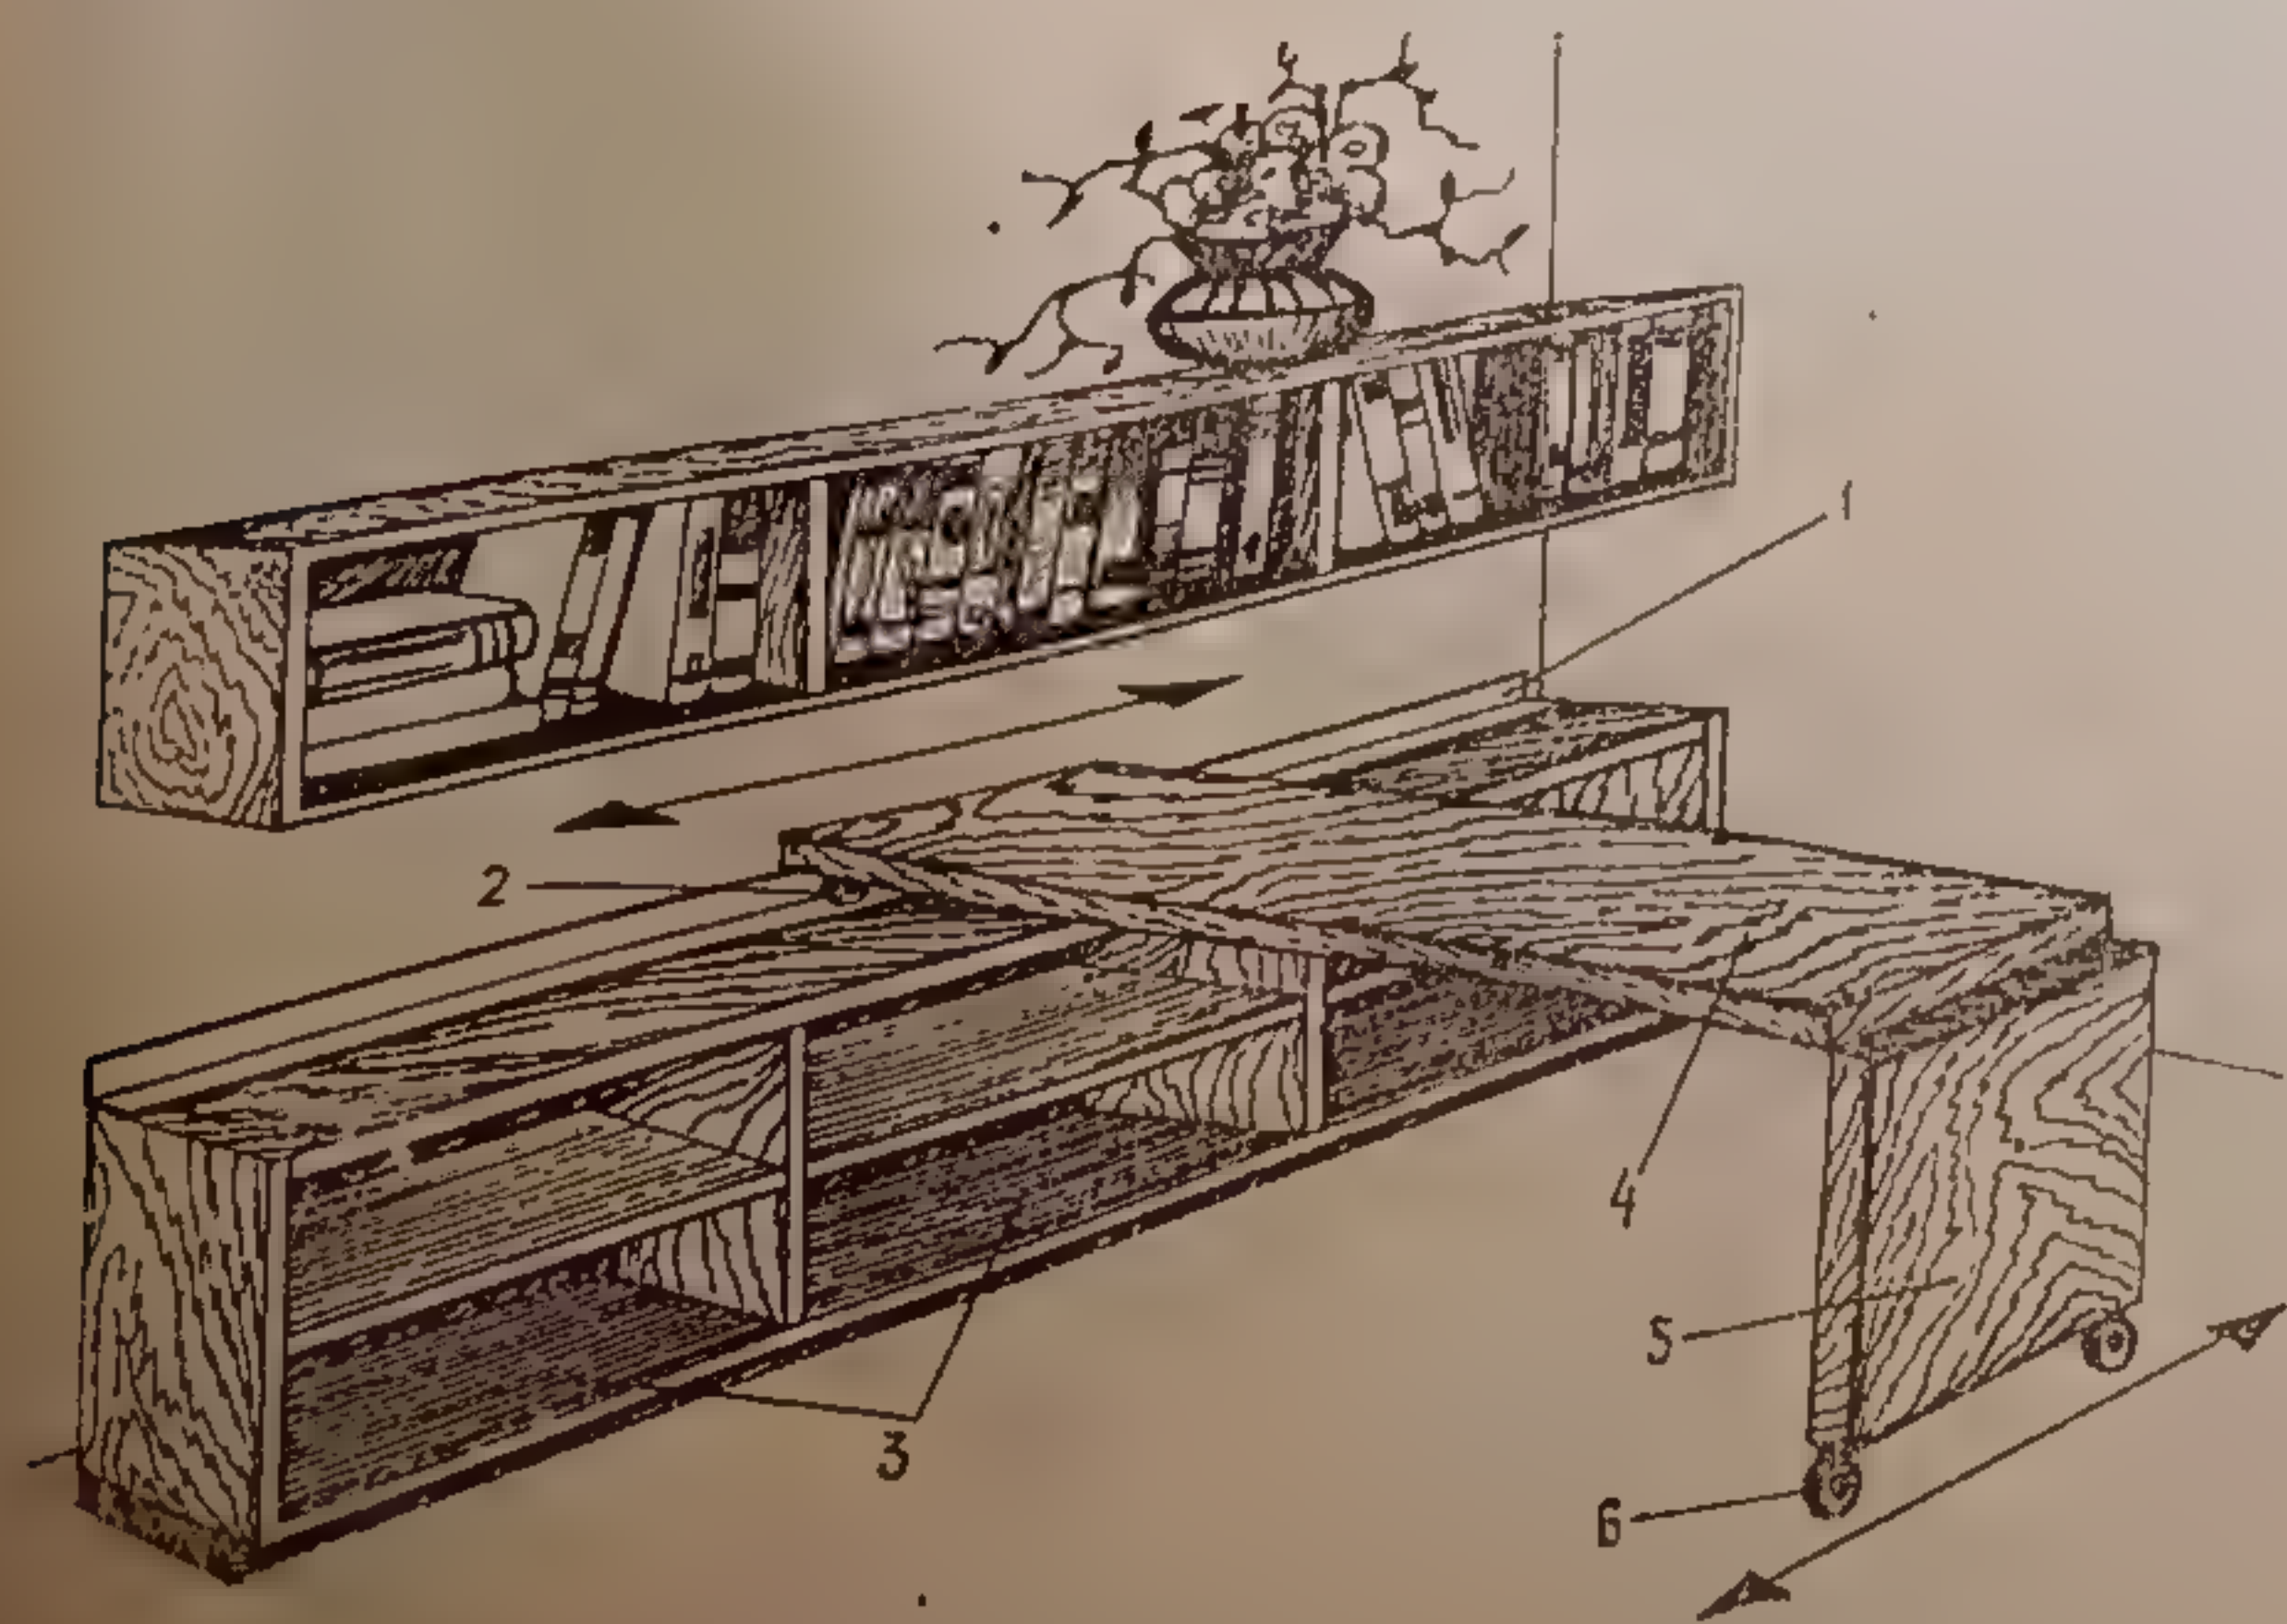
Передвижной рабочий стол: 1 — направляющая; 2 — подшипник; 3 — полки книжные; 4 — столешница; 5 — опорная боковина; 6 — катки
